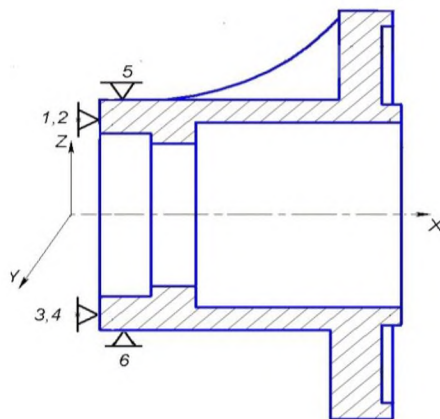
Теоретична схема базування заготовки при першій операції
